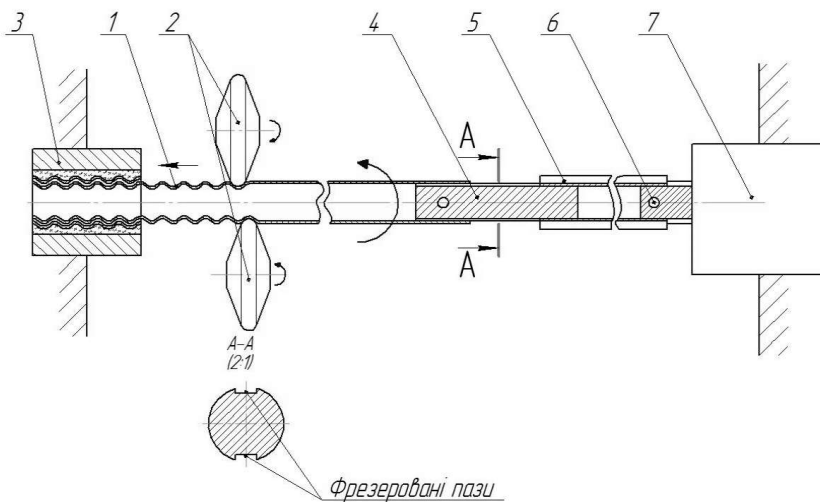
Принципова схема отримання гвинтоподібних труб шляхом трьох роликового обкочування з калібруванням: 1 – труба; 2 – ролики обкатної головки; 3 – диск з внутрішньою різьбою; 4 – стержень з пазами; 5 – допоміжна труба з пазами; 6 – гвинт; 7 – мотор – редуктор
